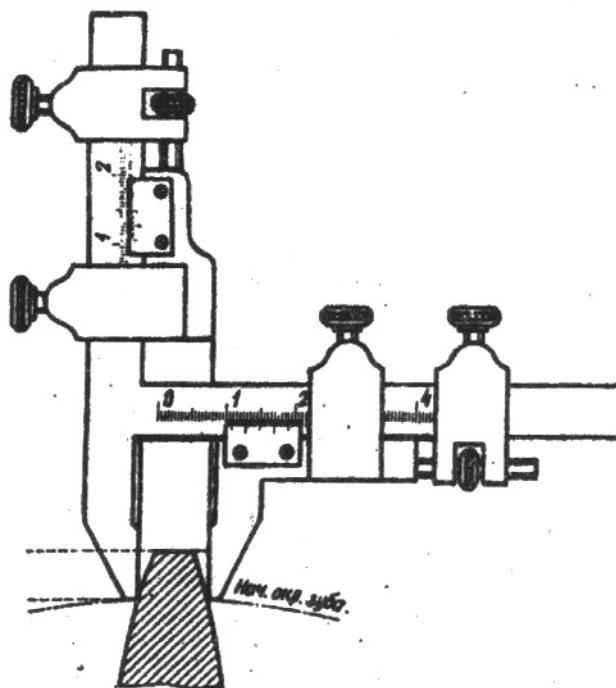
Схема замера зубчатого колеса с помощью штангенциркуля
